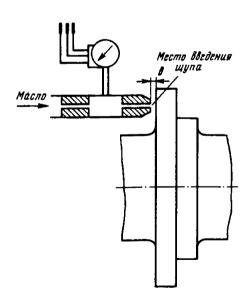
Схема гидравлической защиты от осевого сдвига ротора
